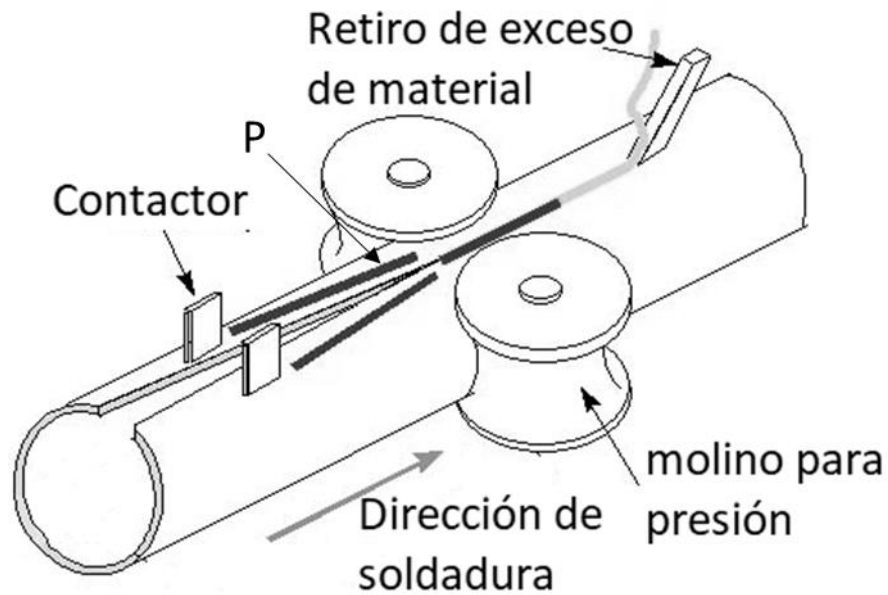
Proceso de soldadura ERW para tuberías. [24]
